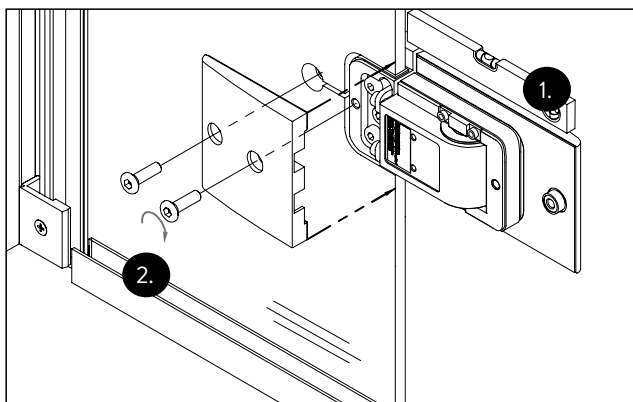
Montage des paumelles à rappel de la porte battante au panneau latéral
